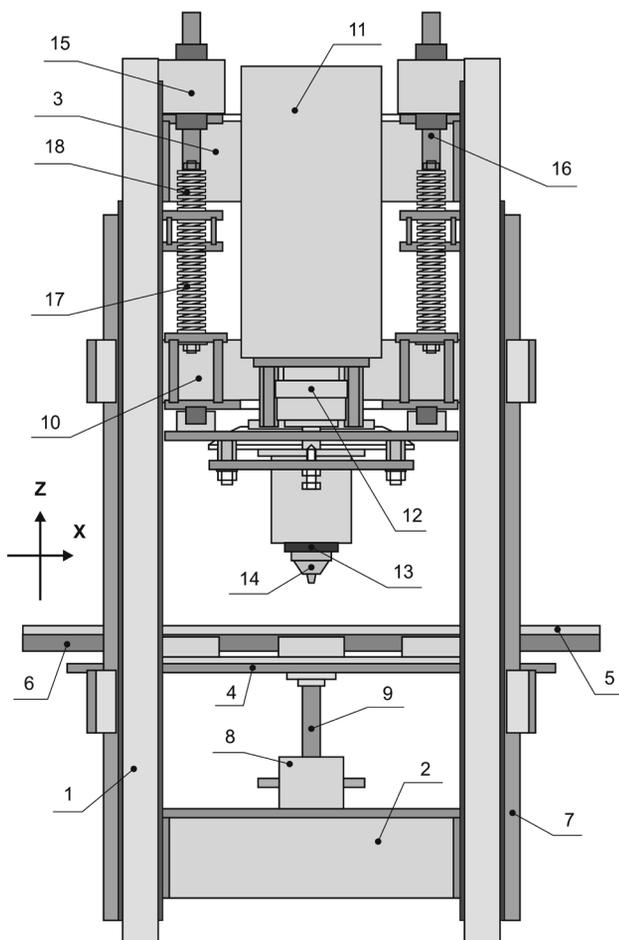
Основные элементы установки фрикционной сварки. Электродвигатели приводов подачи сварочного стола (ось X) и шпинделя (ось Y) не показаны
